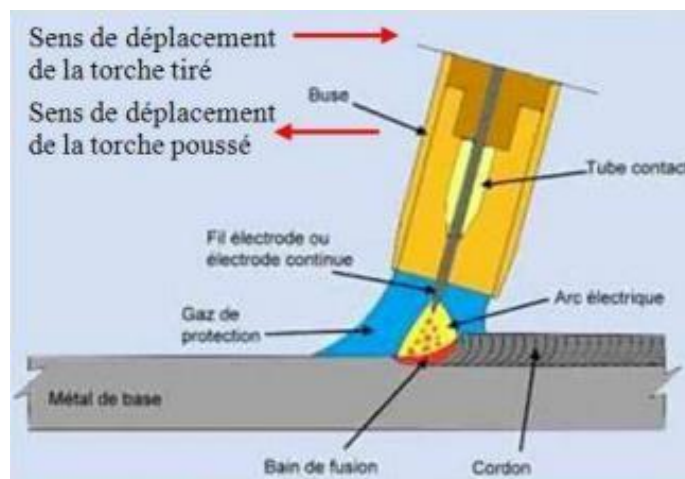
Procédés de soudage MIG/MAG[13]
